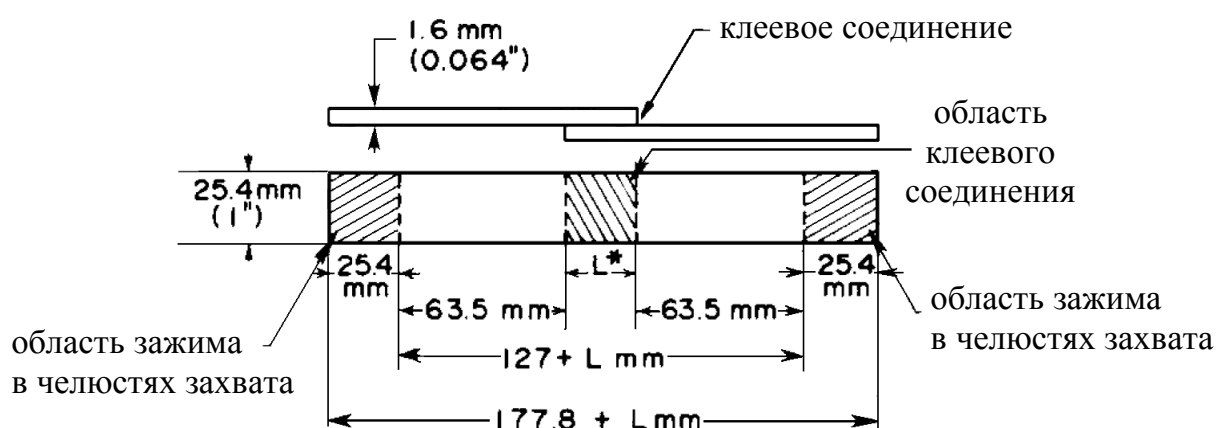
Форма и размеры (в мм) образца согласно ASTM D1002–10
